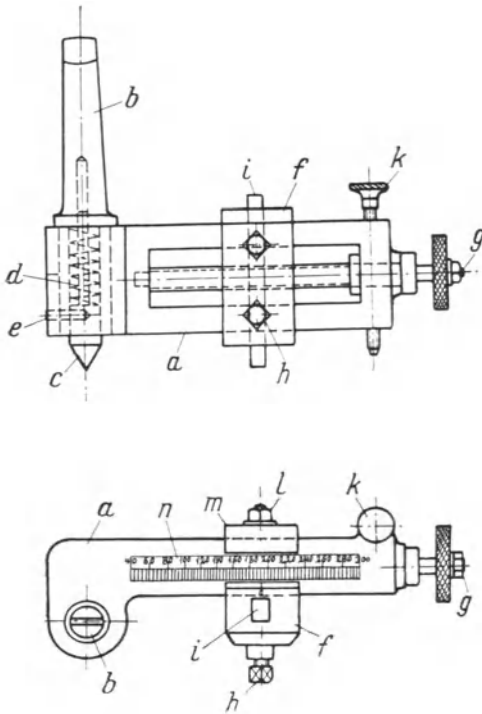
Ausschneidevorrichtung für Blechplatten.
